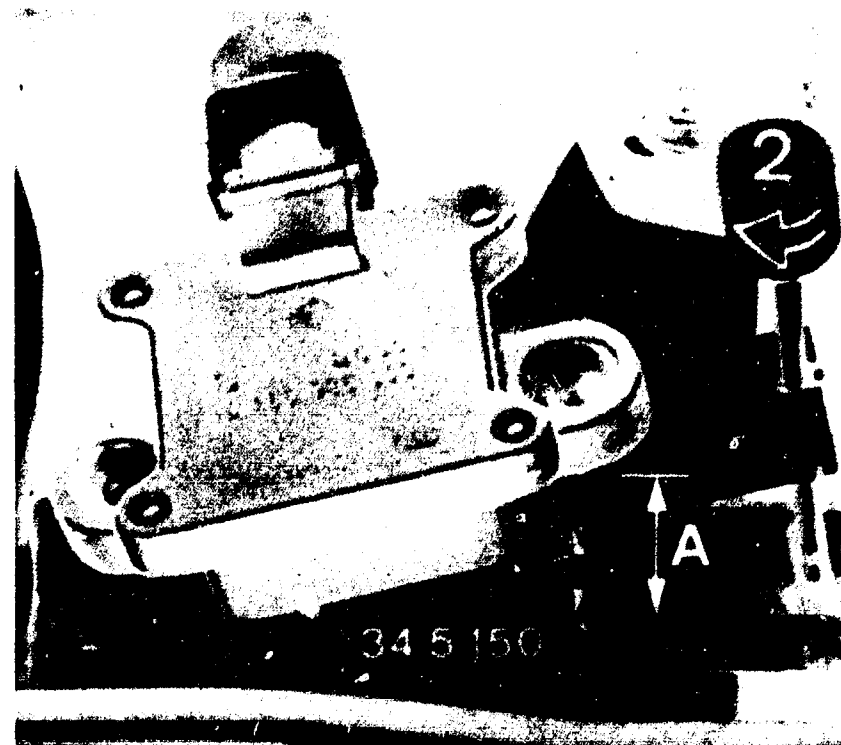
Das Prüfen und Einstellen des Beschleunigungssensors. A Sollwert 26,5...33,0mm – 2 Verstelle Schraube des Neigungsmessers 345150.
